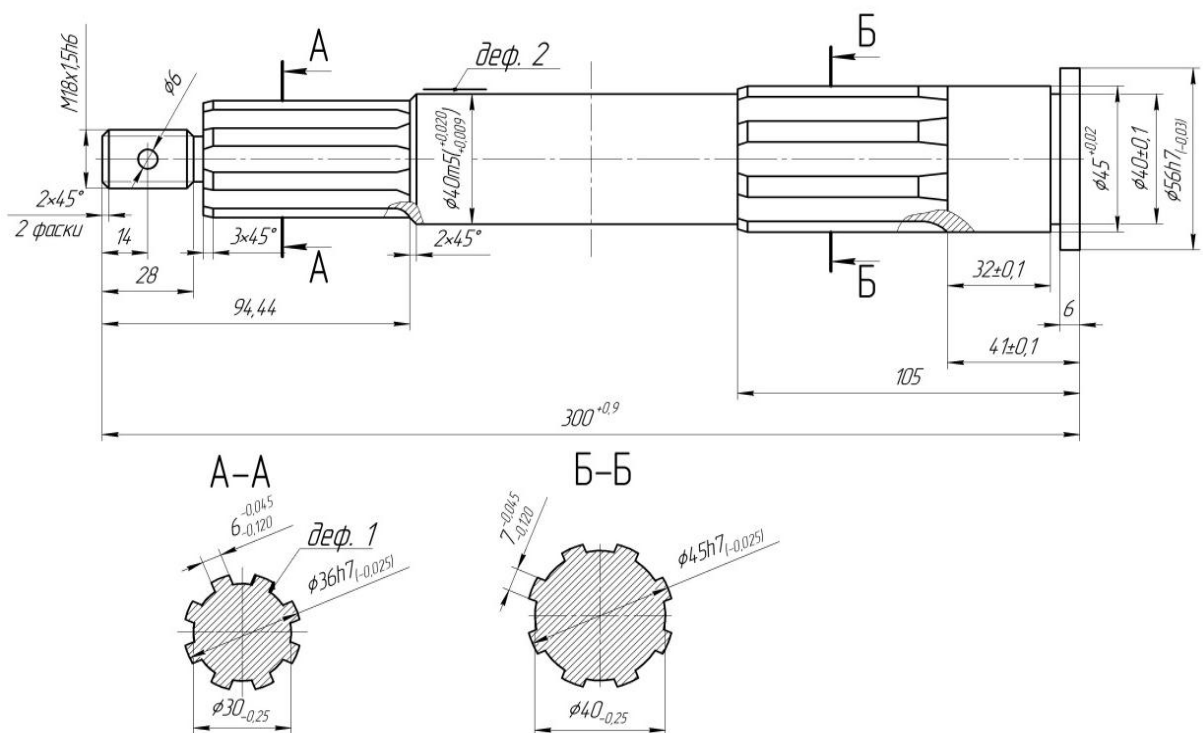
Бази механічної обробки деталі «Вал ведучий»
